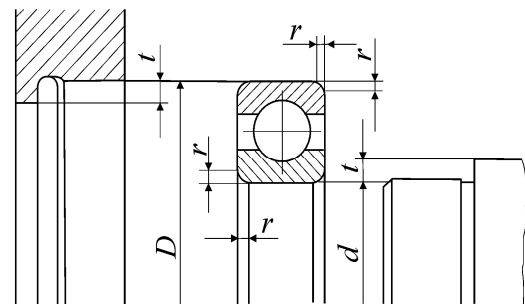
Схема й розміри заплечиків для правильного установлення підшипника
